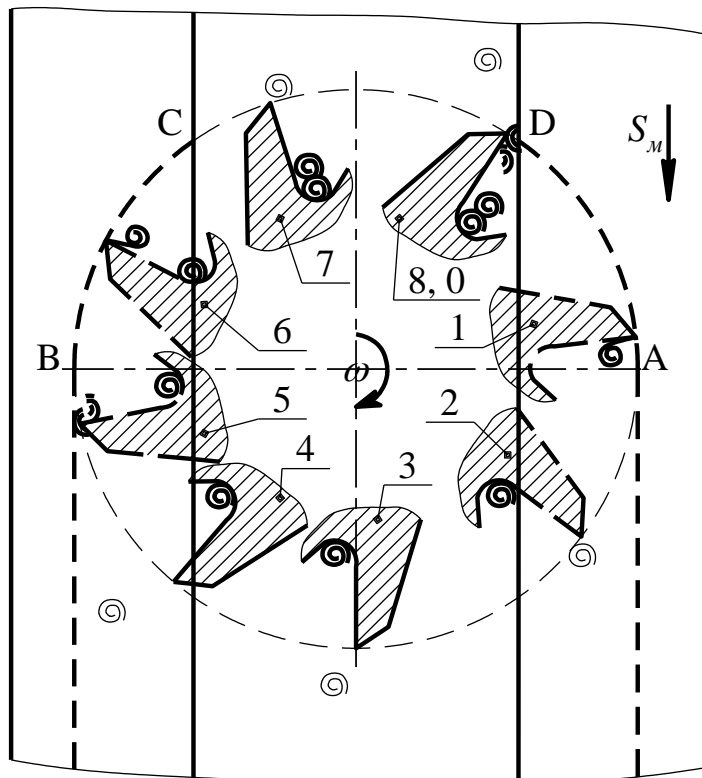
Перемещение элемента стружки в рабочем пространстве фрезы (1...8 - положения зуба в течение одного оборота фрезы)
